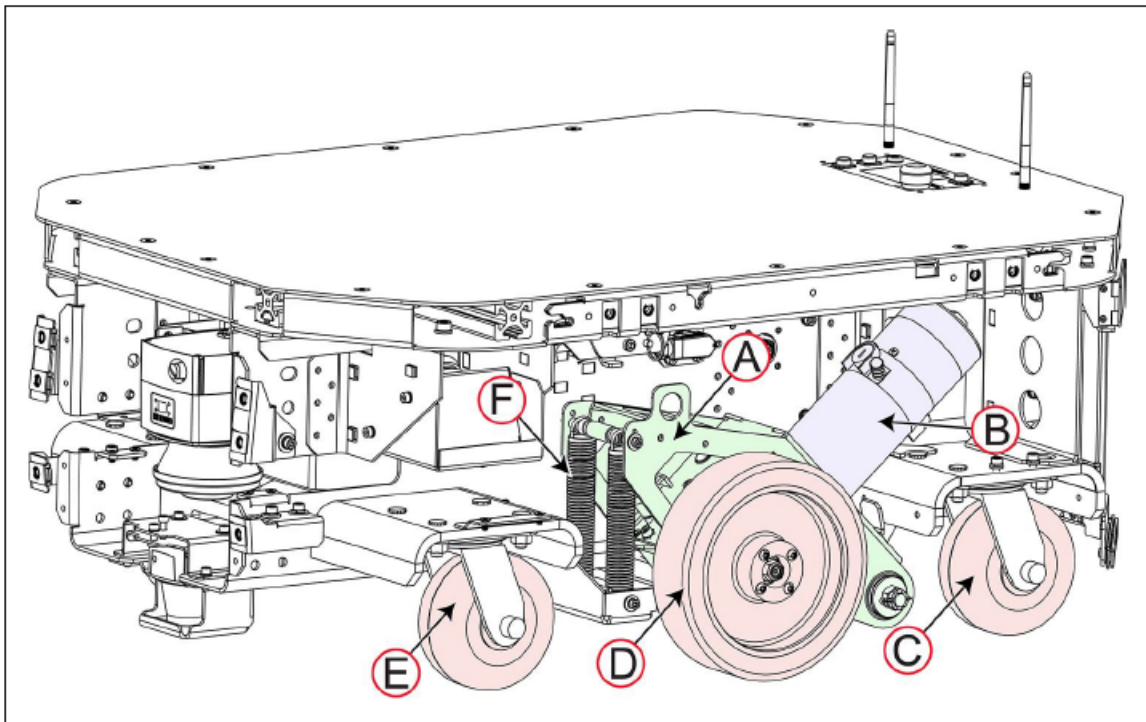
Drivenhet i LD-250 (höljen borttagna)
